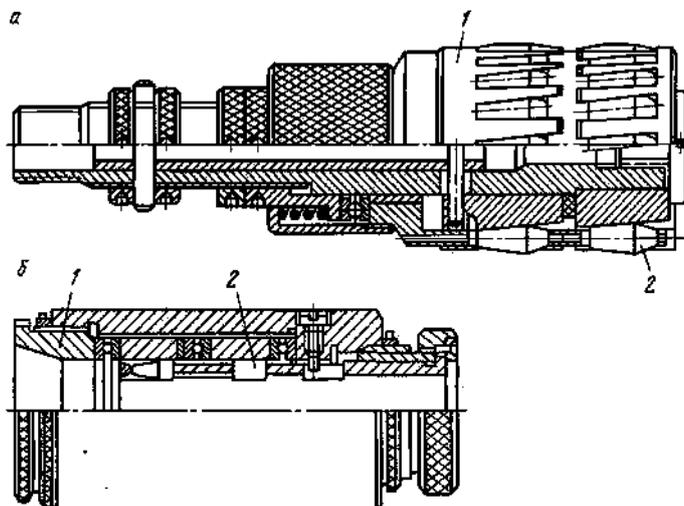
Инструмент для размерно-чистовой обработки ППД внутренних отверстий цилиндров (а) и штоков (б): 1 - корпус инструмента; 2 - ролики
